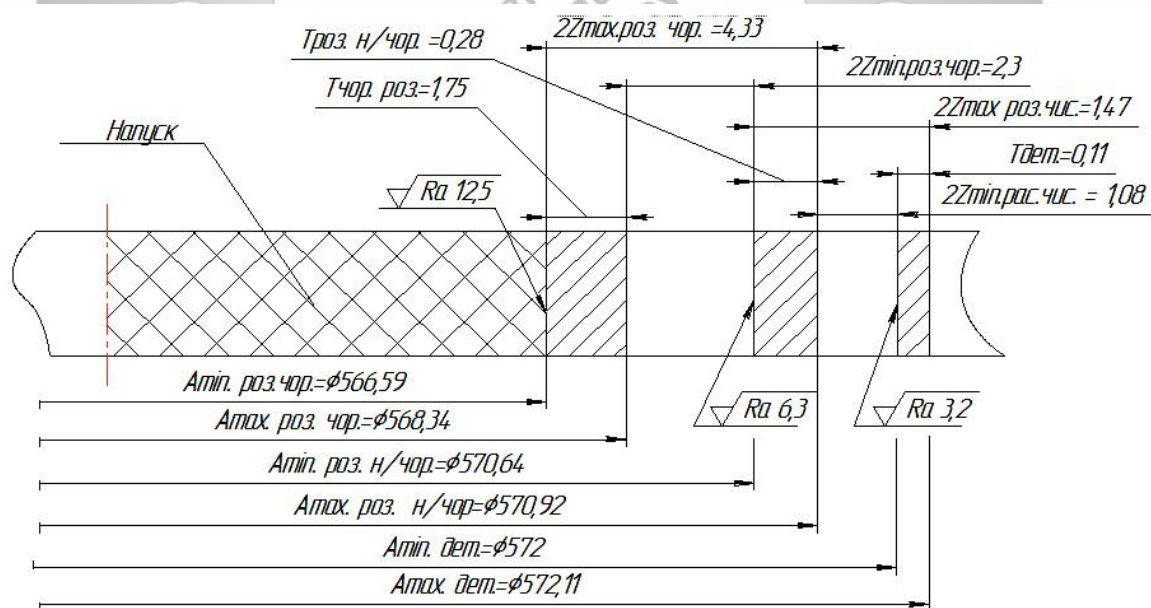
Схема розміщення припусків та допусків на оброблення поверхні  $\phi 572H8$
